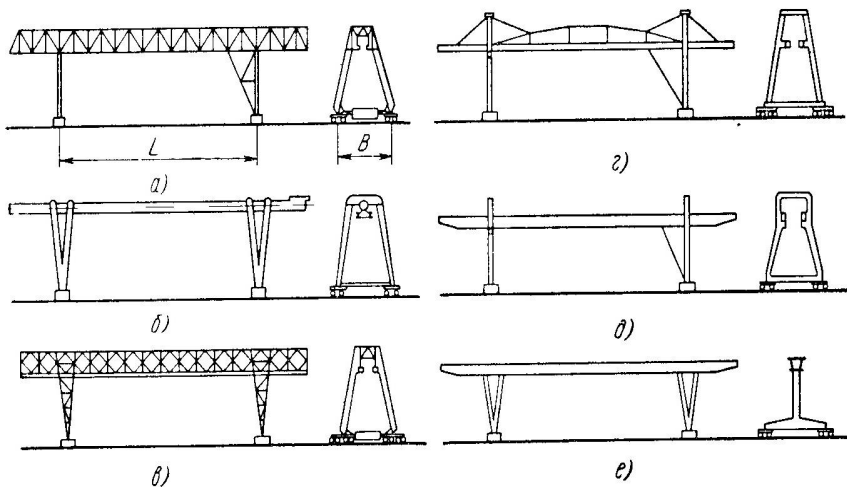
Схеми металоконструкцій перевантажувачів:
